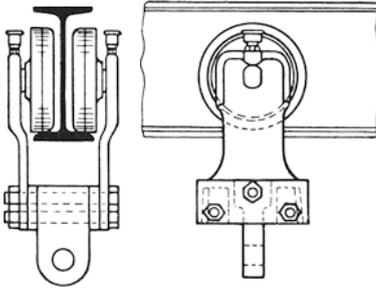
Unterflanschlaufwerk mit zwei Laufrädern (Kaiser).
